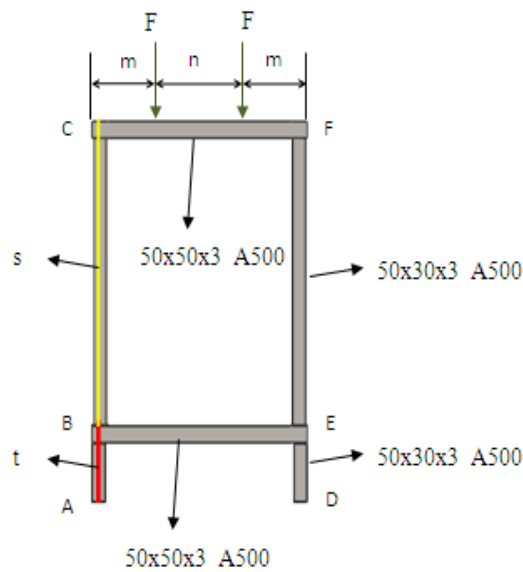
Dimensiones de la estructura de soporte-conjunto
